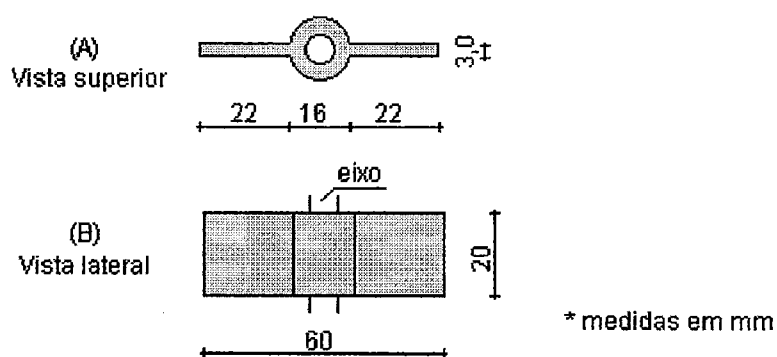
Esquema das paletas utilizadas para homogeneização.
